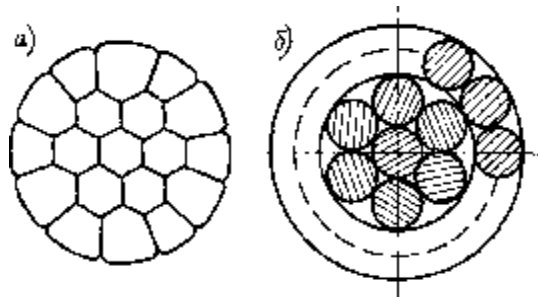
Круглая токопроводящая жила правильной геометрической скрутки: а) –уплотненная; б) – неуплотненная.
